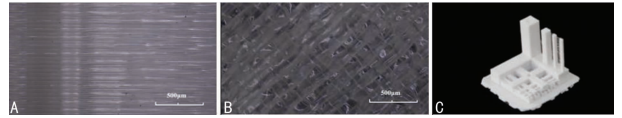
A:X-Z 平面熔纤打印平面;B:X-Y 平面熔纤打印平面;C:解析度模型外形。
